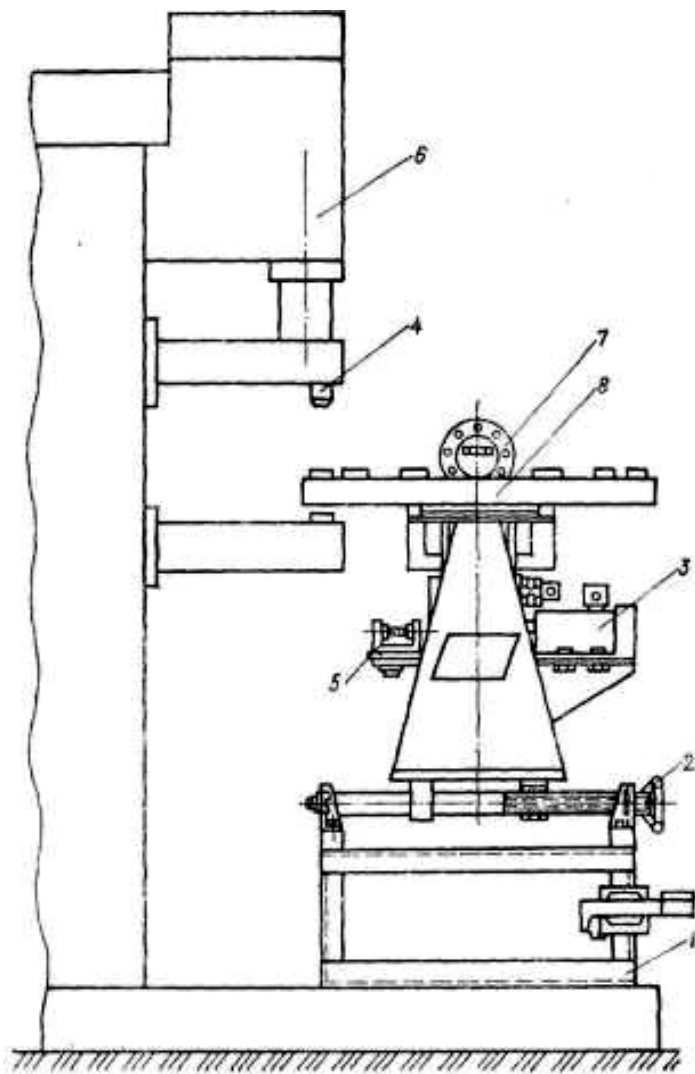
Установка для контактной сварки с многопозиционным поворотным столом:
